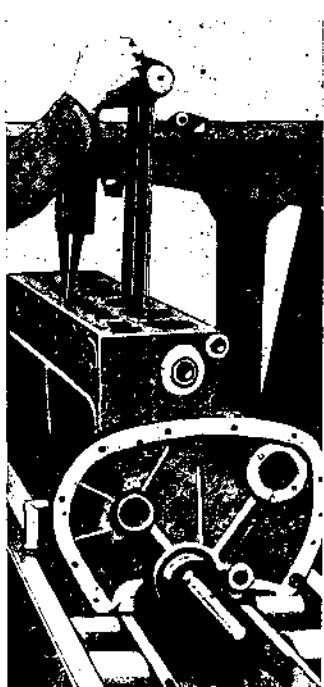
Приспособление для проверки перпендикулярности осей цилиндров оси вала.
